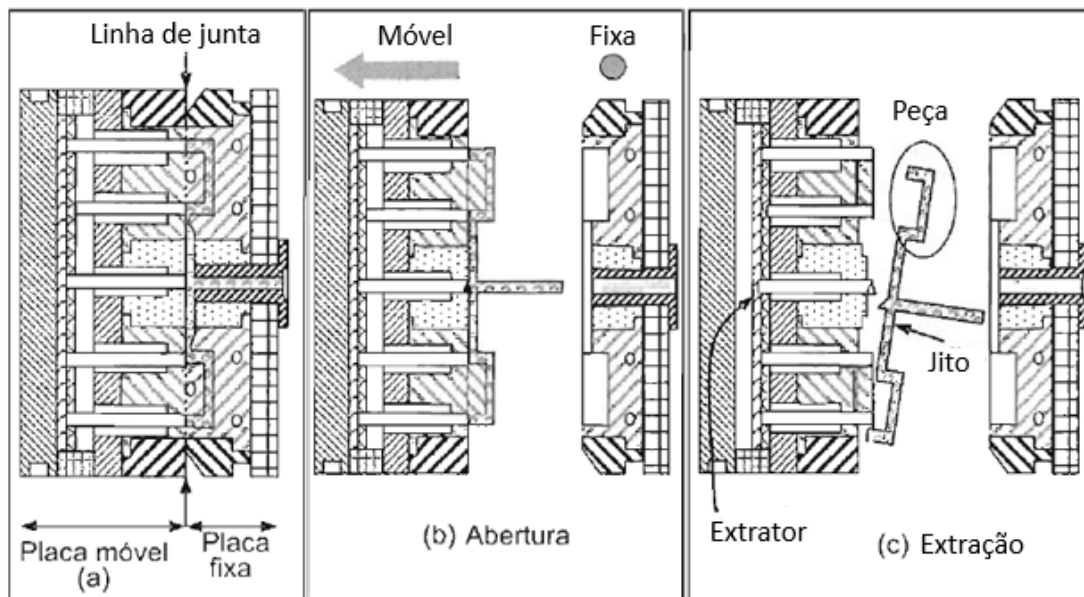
Molde de duas placas: a) molde fechado, b) molde aberto e c) acionado o sistema de extração do molde e peça a cair (Manrich, 2005)
